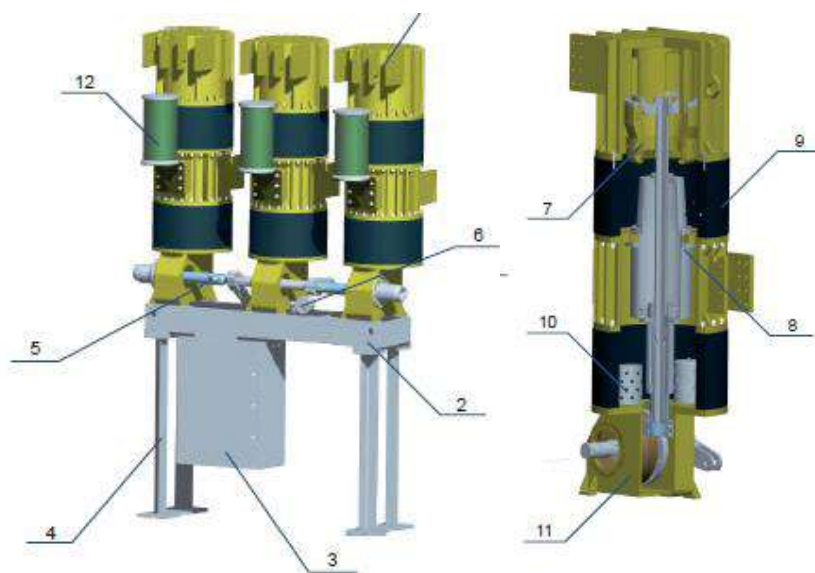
Устройство и внешний вид выключателя ВГП -110
